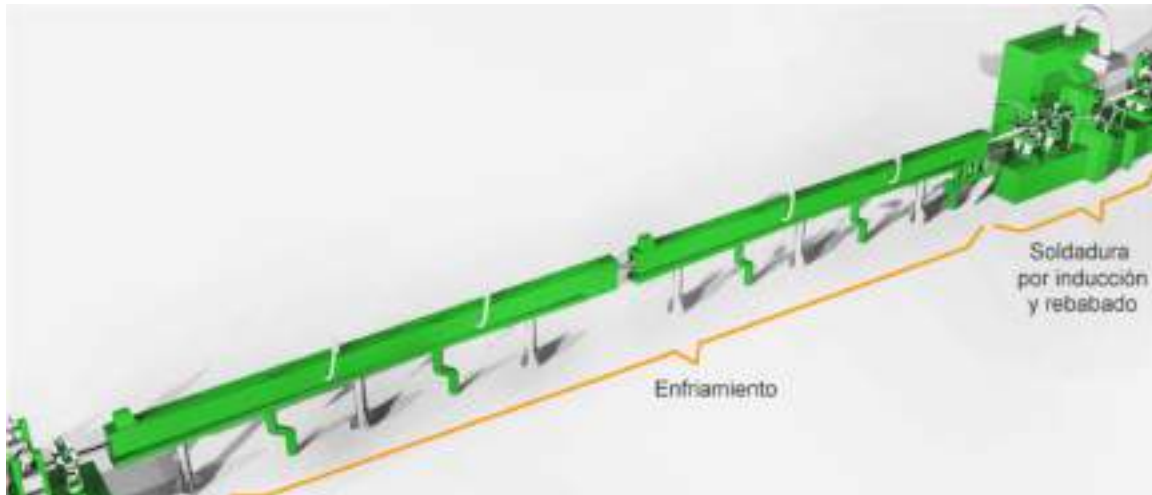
Etapas de soldadura, rebabado y enfriamiento.
